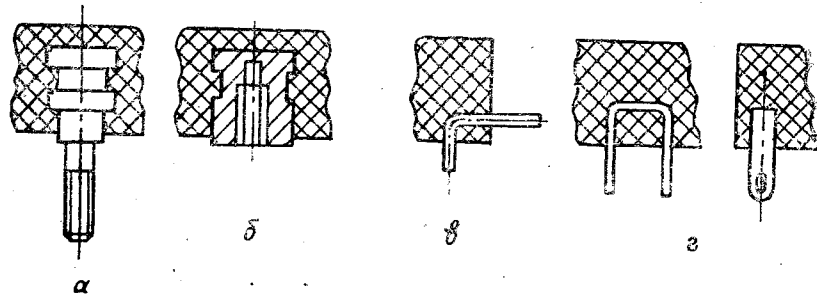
Армування пластмасових заготовок: а — штирями; б — буксами; в — дротиками; г — пелюстками.
